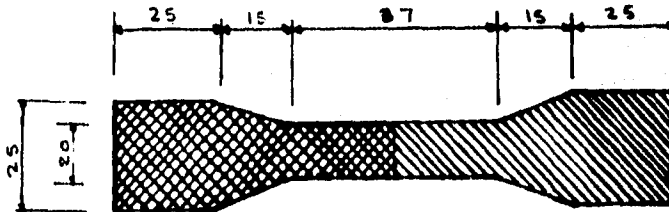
Dimensiones y forma de las probetas Aluminio-Latón para ensayos.
